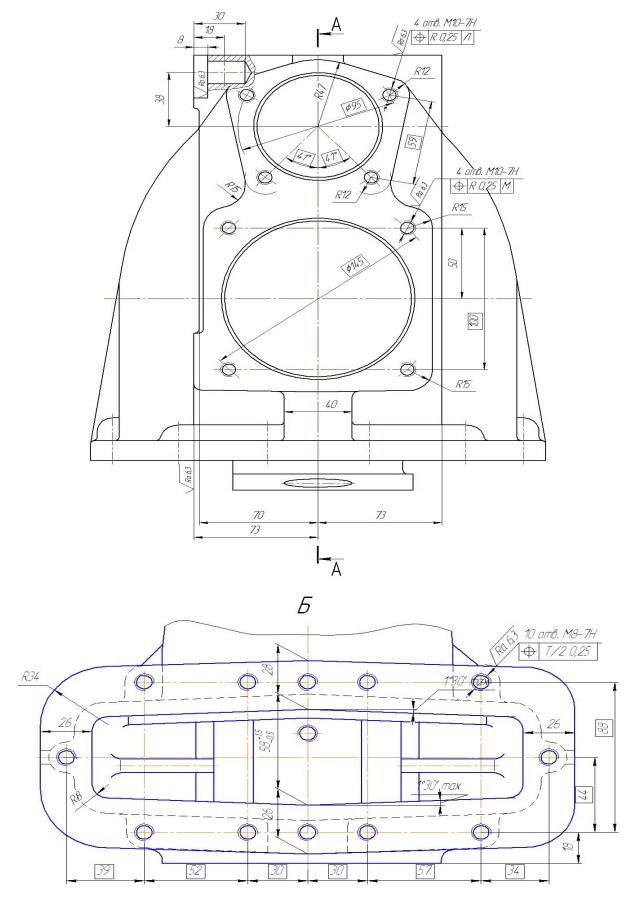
Чертеж детали «Корпус редуктора» (см. также с. 187, 188)
